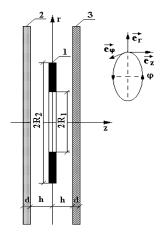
Расчетная модель в цилиндрической системе координат (e_r, e_{ϕ}, e_z — направляющие орты), 1 — виток индуктора (R_1, R_2 — внутренний и внешний радиусы; 2 — экран (d — толщина); 3 — заготовка (d — толщина); h — расстоянии от витка индуктора до экрана или заготовки.
